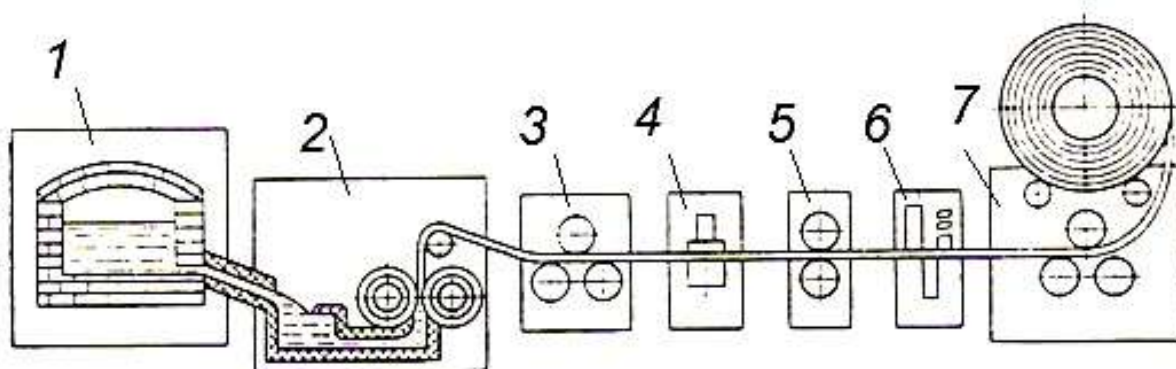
Литейно-прокатный агрегат конструкции ВНИИМетМаш для производства алюминиевой полосы: 1 – миксер; 2 – валковый кристаллизатор; 3 – правильная машина; 4 – центрирующие ролики; 5 – машина для обрезки кромки; 6 – гильотинные ножницы; 7 – моталка
